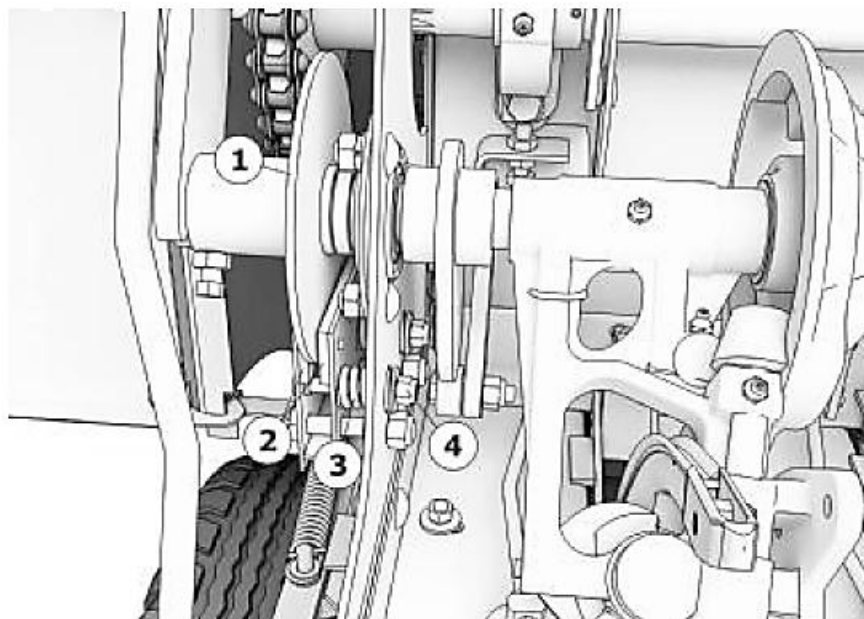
Тормоз обвязывающего механизма: 1 – диск; 2 – пластина фрикционная; 3 – пружина; 4 – гайка
